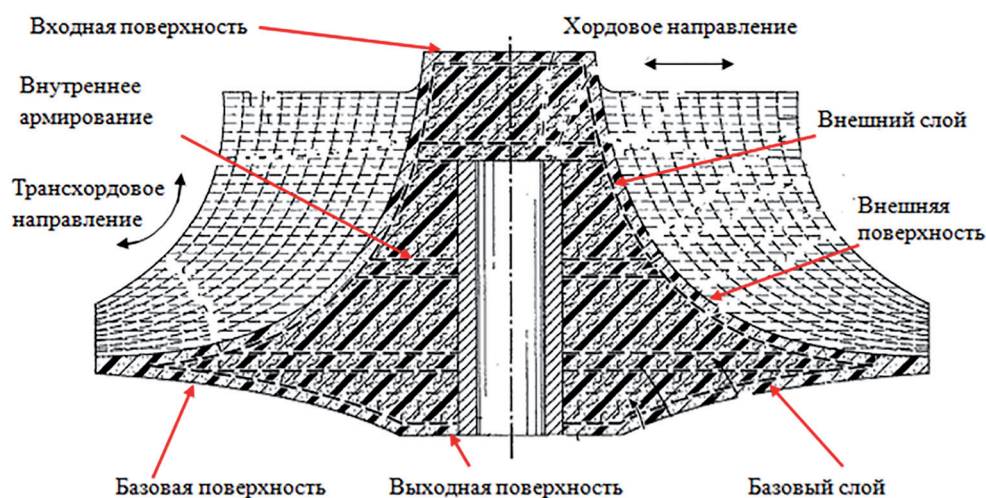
Схема армирующей структуры рабочего колеса компрессора ТК [12]
